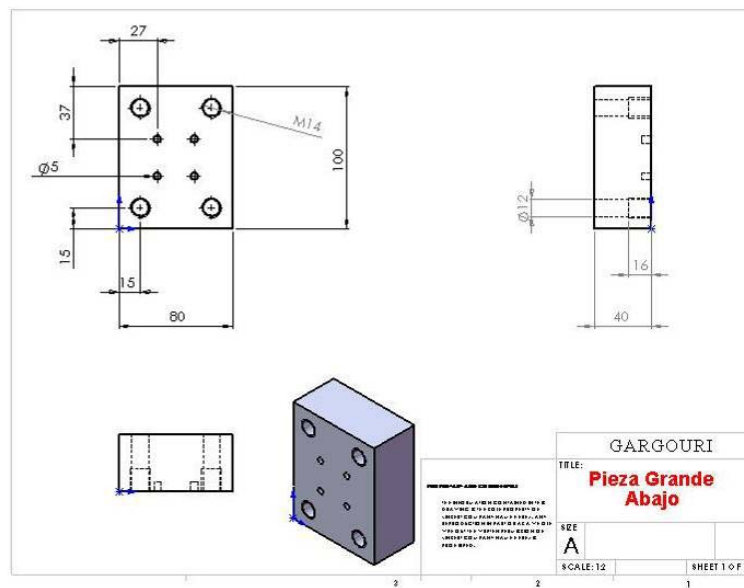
Vistas y dimensiones de una de las piezas del montaje: pieza grande abajo
